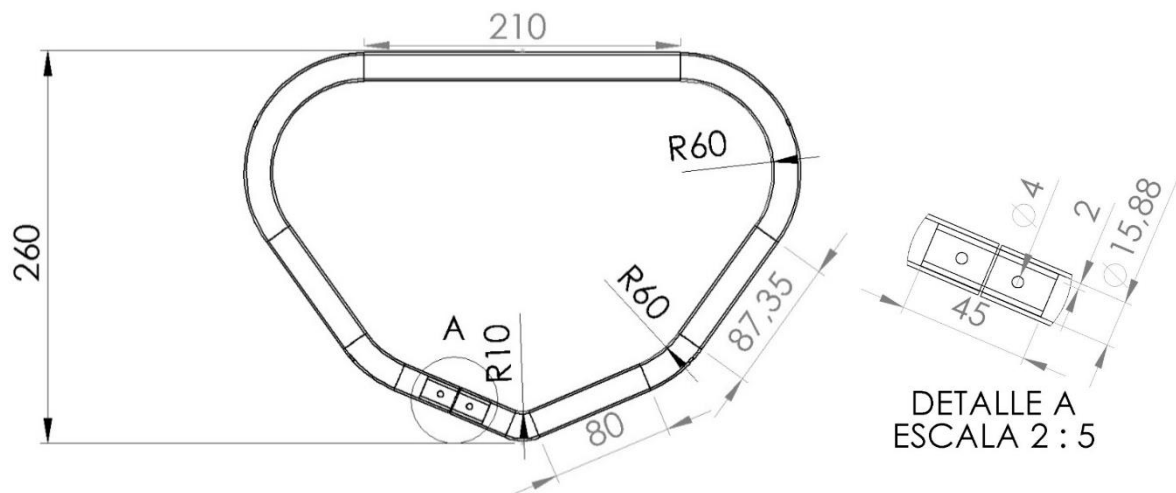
20 Plano cuaderna de popa
